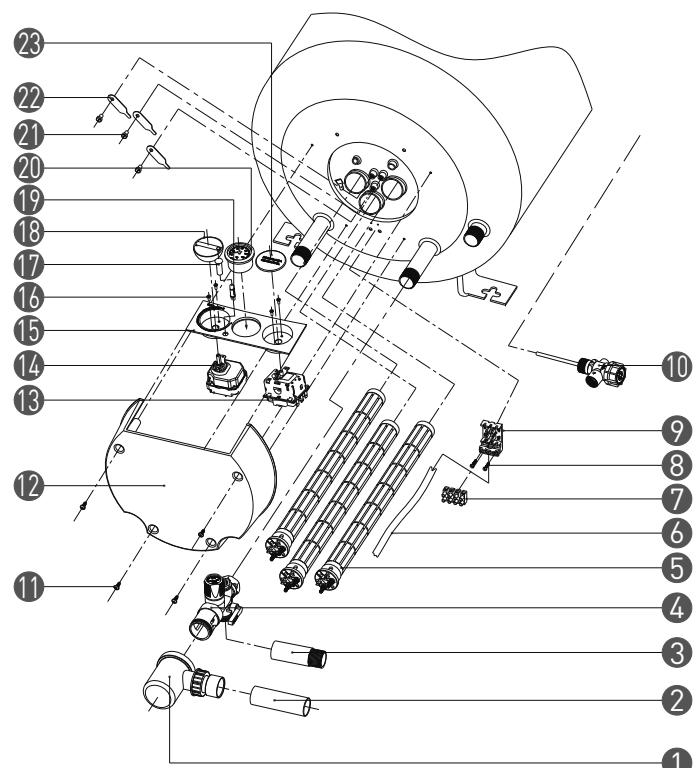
Montagem Grupo Eléctrico e Hidráulico
